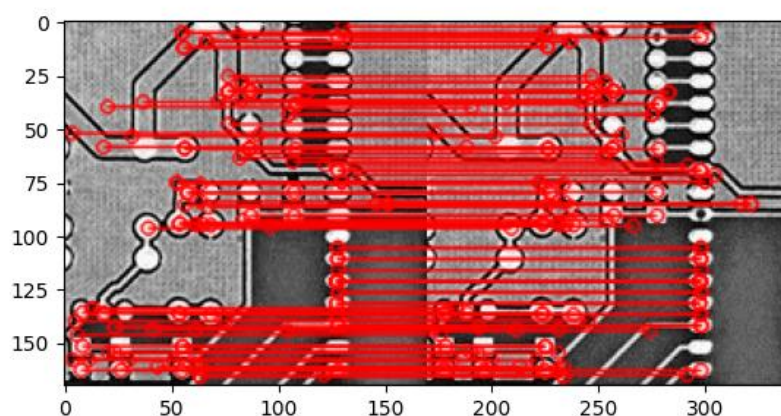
PCB 标准图像和缺陷图像采用 SURF 进行配准
